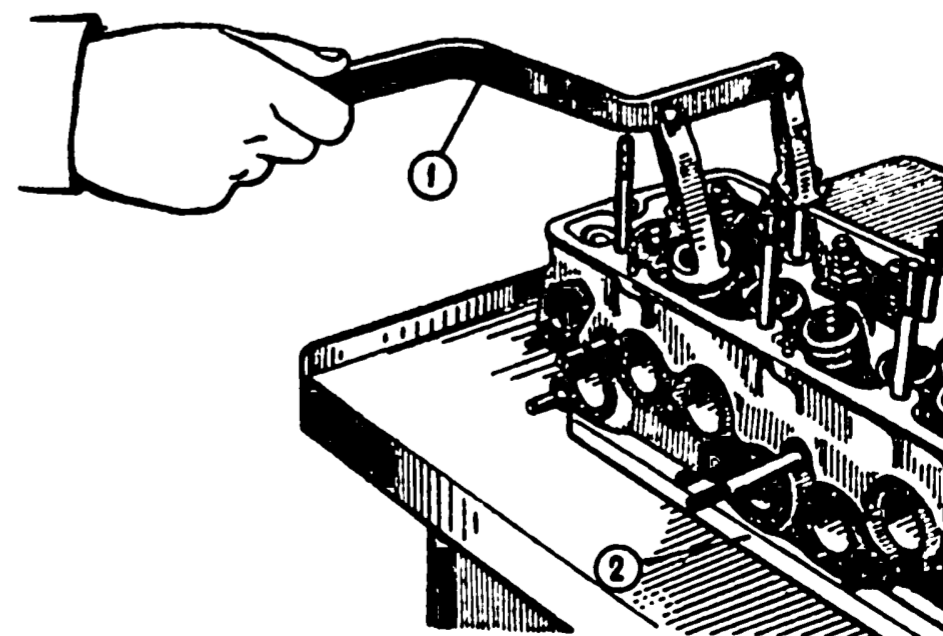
Снятие пружин клапанов: 1 - приспособление А.60311/Р; 2 - монтажная доска А.60335
